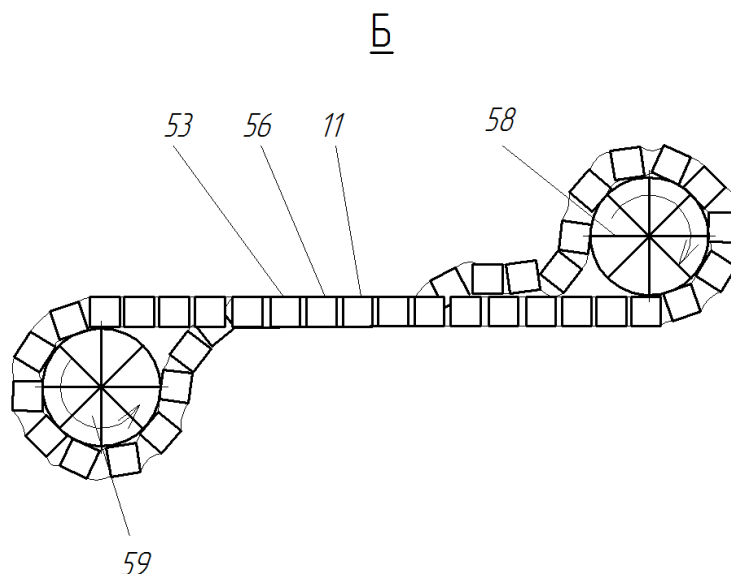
Гидростатический двигатель (схема, вид сверху)
